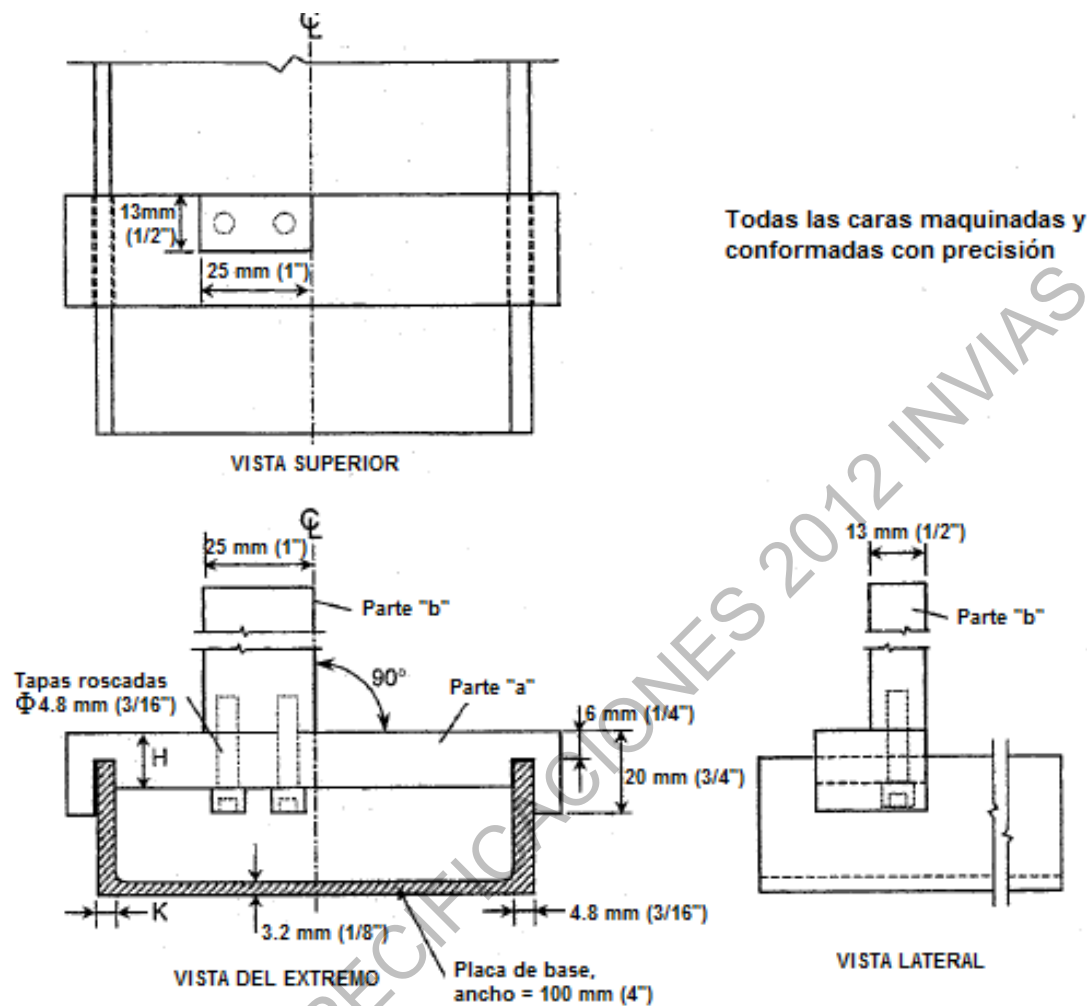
2. Plano detallado de un equipo adecuado para hacer las marcas de las bases, usado para el alineamiento del espécimen
